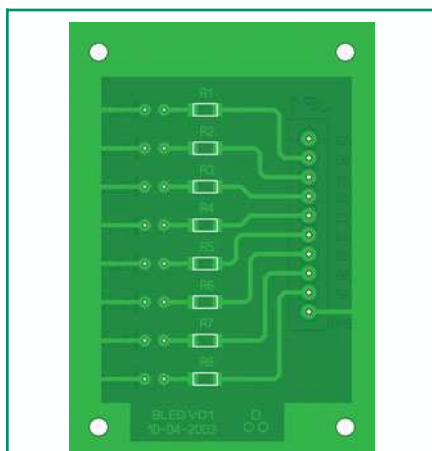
Piano di montaggio lato saldature del modulo a barra di led
